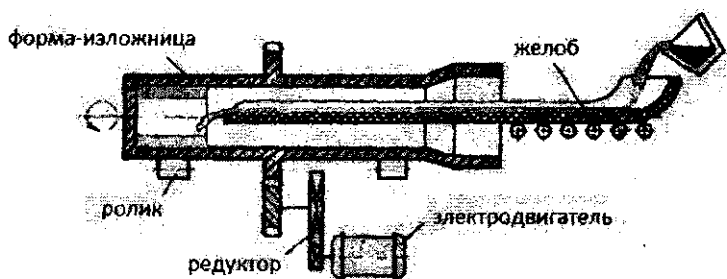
Схема установки для получения отливок методом центробежного литья
